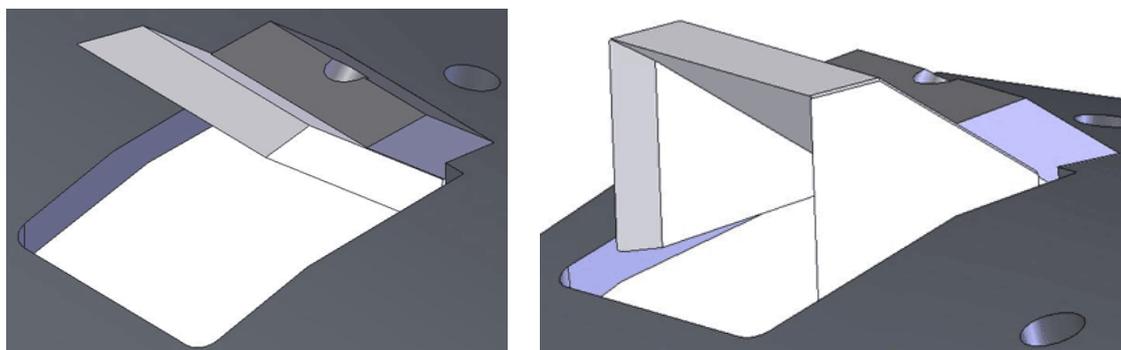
à gauche, couteau droit élargi et à droite couteau en U à trois arêtes de coupe.
